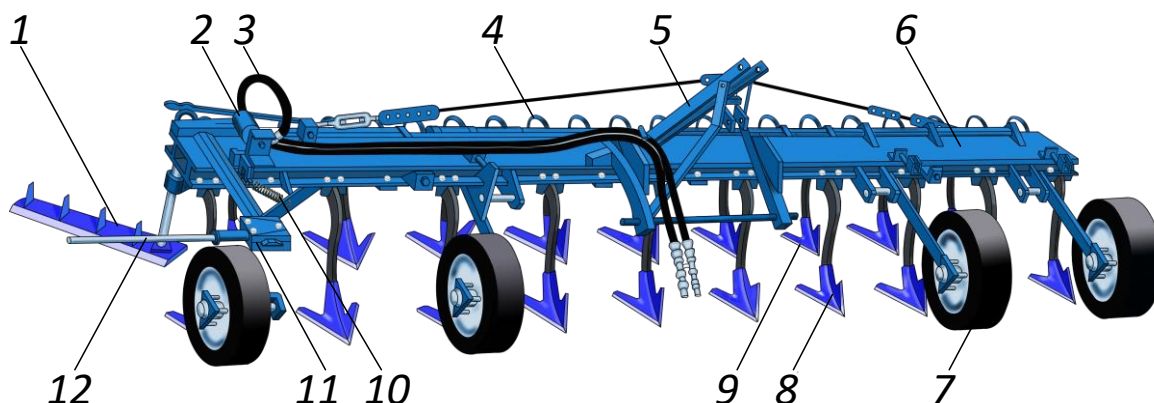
Культиватор садовий гідрофікований КСГ – 5: 1 – поворотна лапа; 2 – гідроциліндр; 3 – рукав гідроприводу поворотної лапи; 4 – борона з пружинними зубами; 5 – начіпний пристрій; 6 – рама; 7 – опорні колеса з гвинтовими механізмами; 8 і 9 – стрілочасті універсальні лапи переднього та заднього ряду; 10 – зворотна пружина; 11 – гідравлічний розподільник керування поворотною лапою; 12 – щуп механізму керування поворотною лапою
